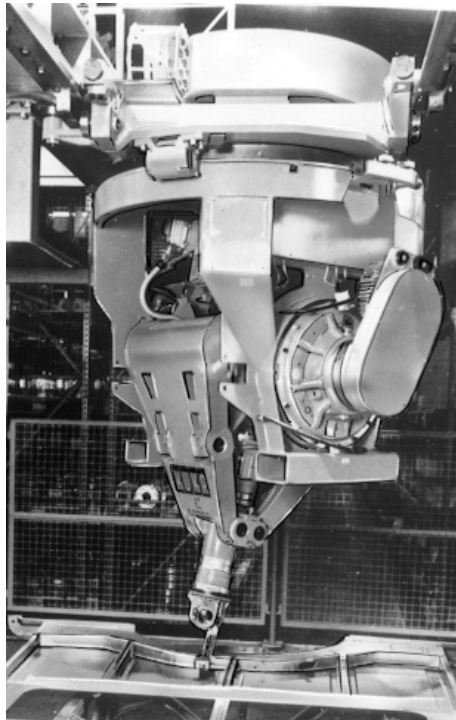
Сварочный робот фирмы КУКА.
